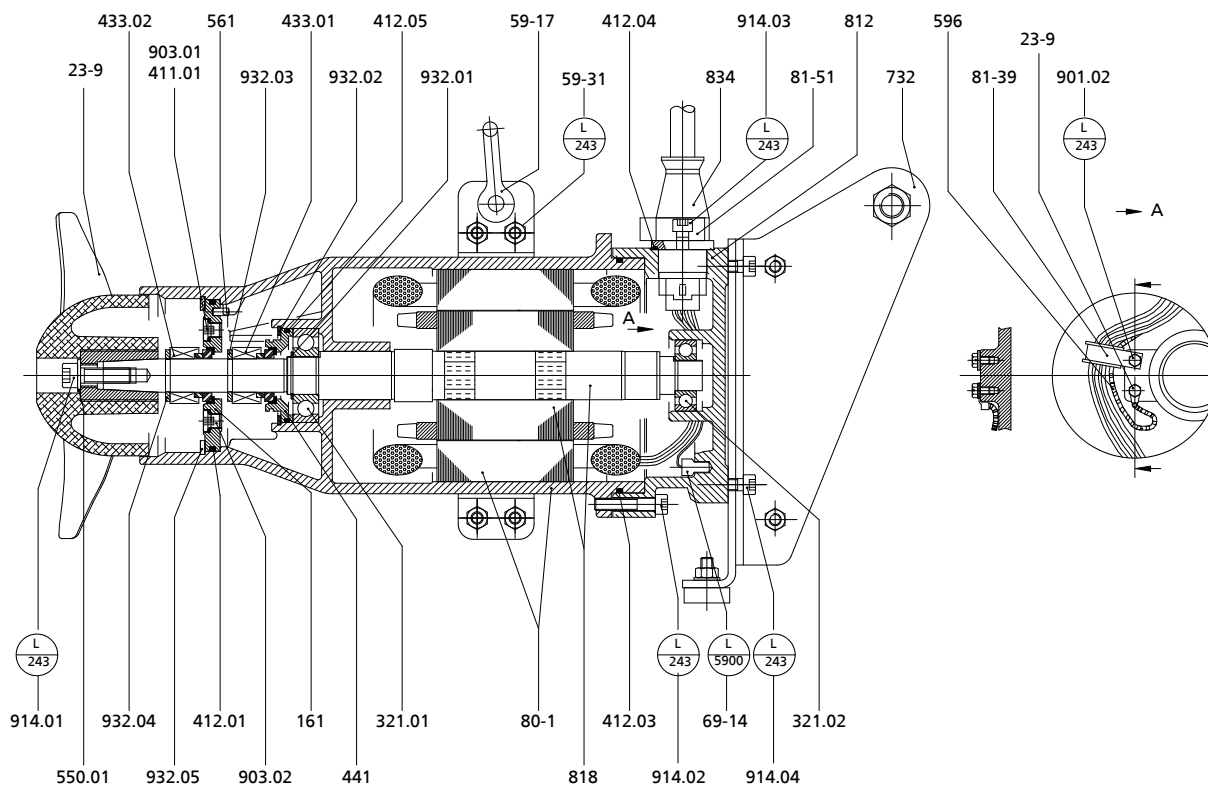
Чертеж общего вида Атаміх 200, материал корпуса двигателя – серый чугун
